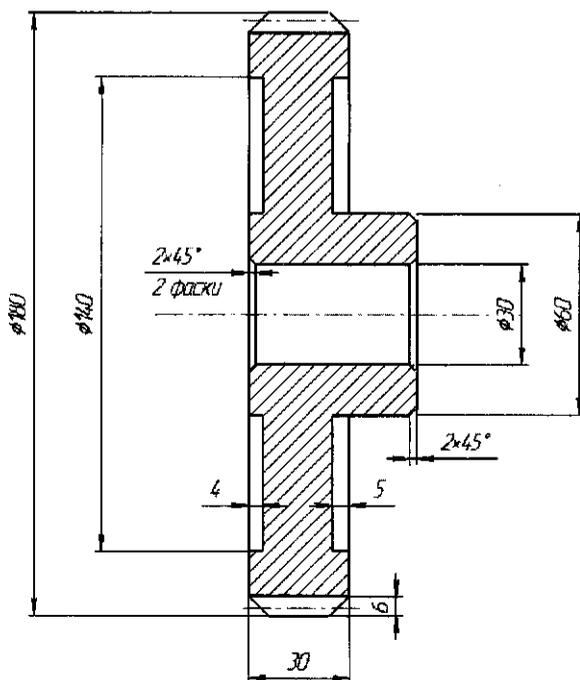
Чертеж зубчатого колеса для задания 31.2
